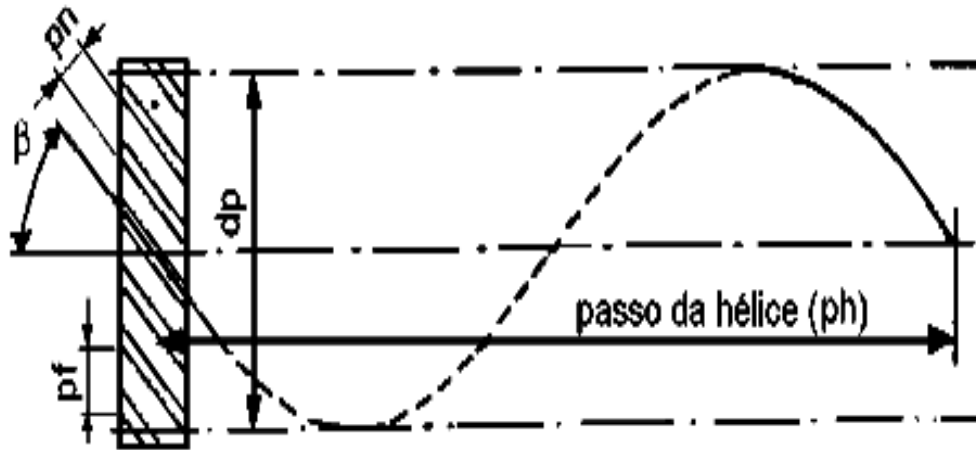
Elementos geométricos de uma engrenagem helicoidal
